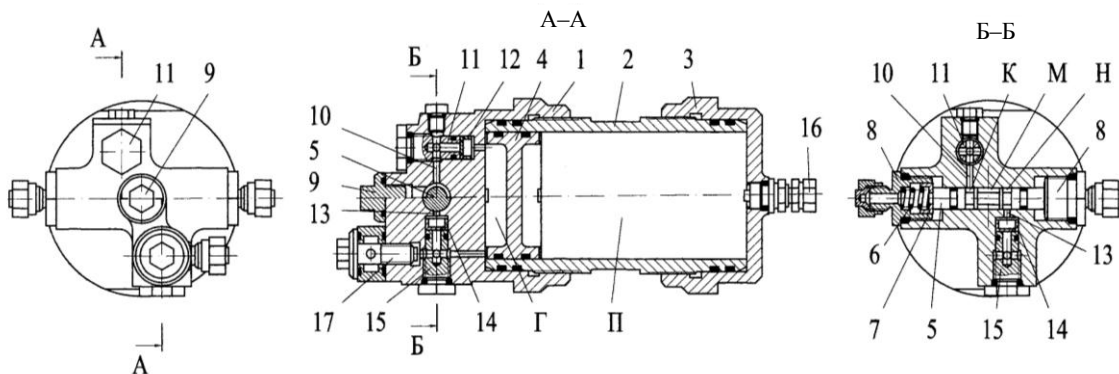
Гидропневматический аккумулятор компенсации: 1 – корпус; 2 – цилиндр; 3 – крышка; 4 – поршень; 5 – золотник; 6 – пружина; 7 – толкатель; 8 – переходник; 9 – пробка; 10, 11, 15 – золотник; 12, 14 – обратный клапан; 13 – канал; 16 – клапан зарядный; 17 – дроссель; 18 – угольник поворотный; Г – гидравлическая полость; П – пневматическая полость; М – центральная полость золотника; К, Н – периферийные полости золотника
